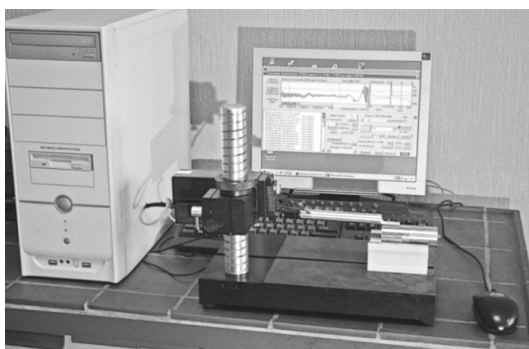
Измерение шероховатости поверхности тестовой детали на профилографе-профилометре 170623 ОАО «Калибр»
